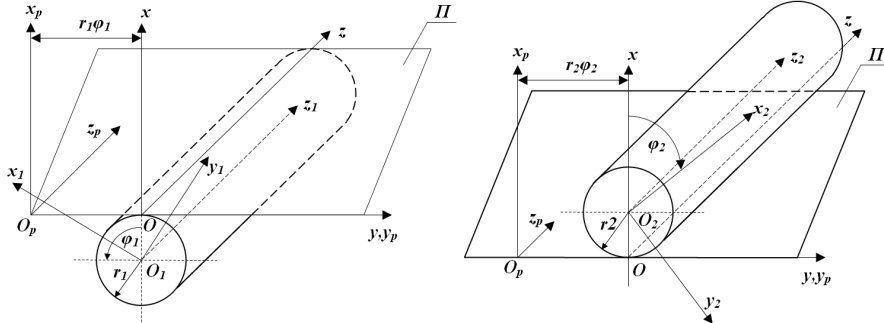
К образованию поверхностей зубьев зубчатых колёс
